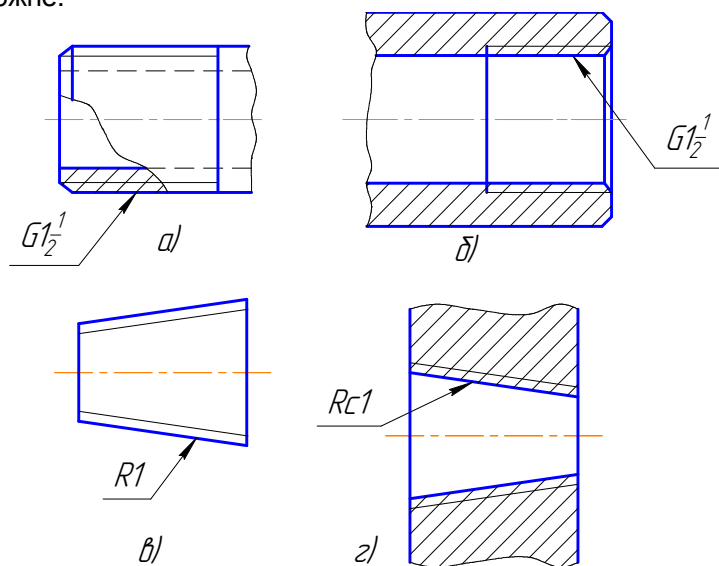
Условные обозначения трубной цилиндрической и конической резьбы:
